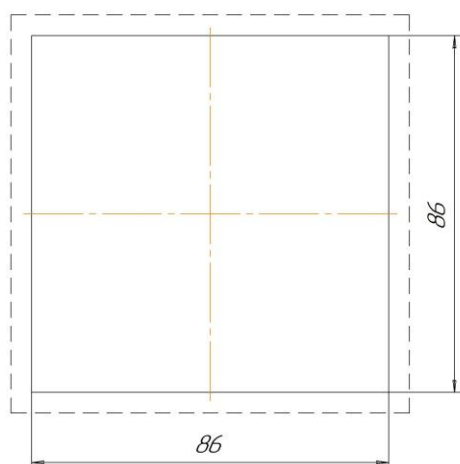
Габаритно-установочный чертеж ЭЛИЗ А50
